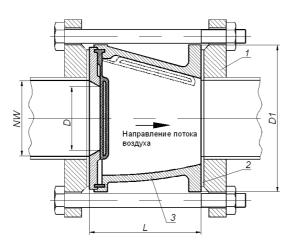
Разрез обратного клапана: 1 - фланцевое соединение; 2 - прокладка; 3 - обратный клапан.
